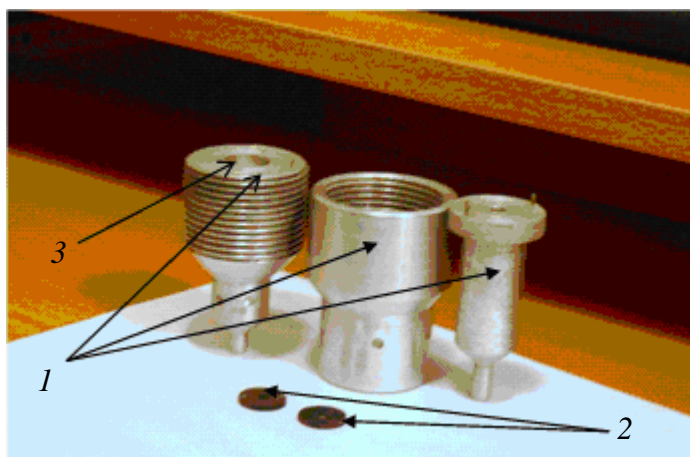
Разработанное устройство для фиксации образца: *1* – алюминиевый фиксатор; *2* – резиновые уплотнения, между которыми помещался образец; *3* – углубление для образца и уплотнений
